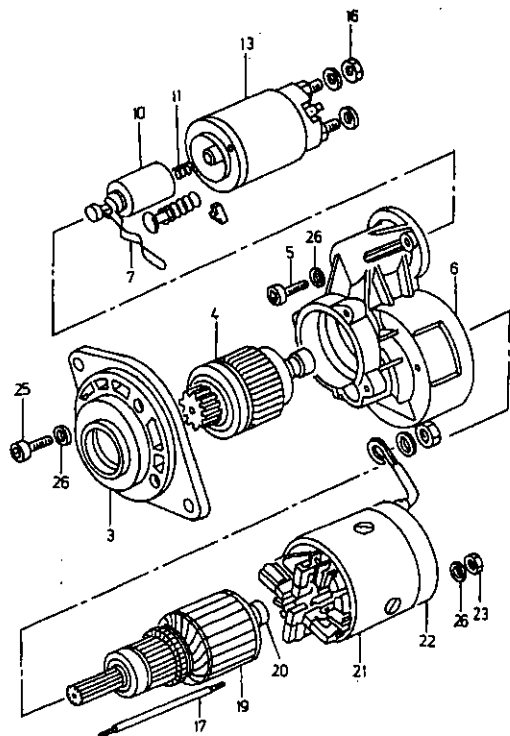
Tvar a základní rozměry spouštěče motoru MAGNETON 12 V - 1 kW (č. v. 443 115 141 310)
